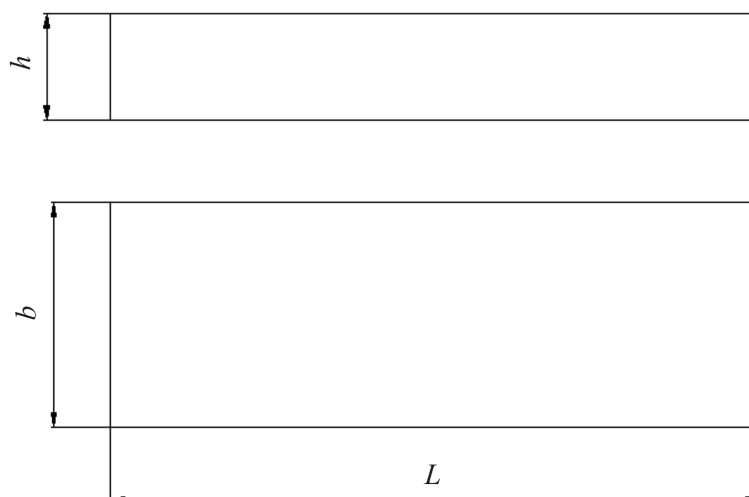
Типовая схема стандартного образца, изготовленного для испытаний на межслоевой сдвиг методом короткой балки
